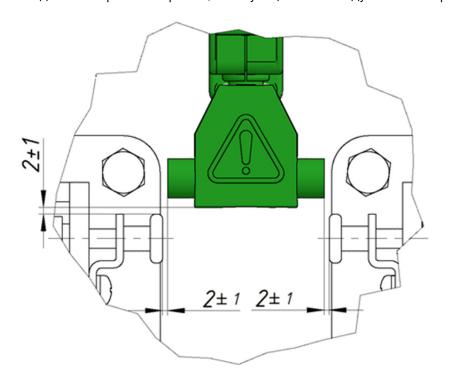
Установка блокиратора со сдвоенными разъеденителями
